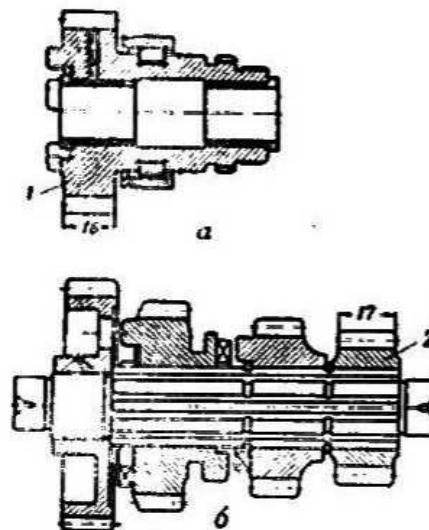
Валики с шестернями коробки перемены передач «ИЖ»:
